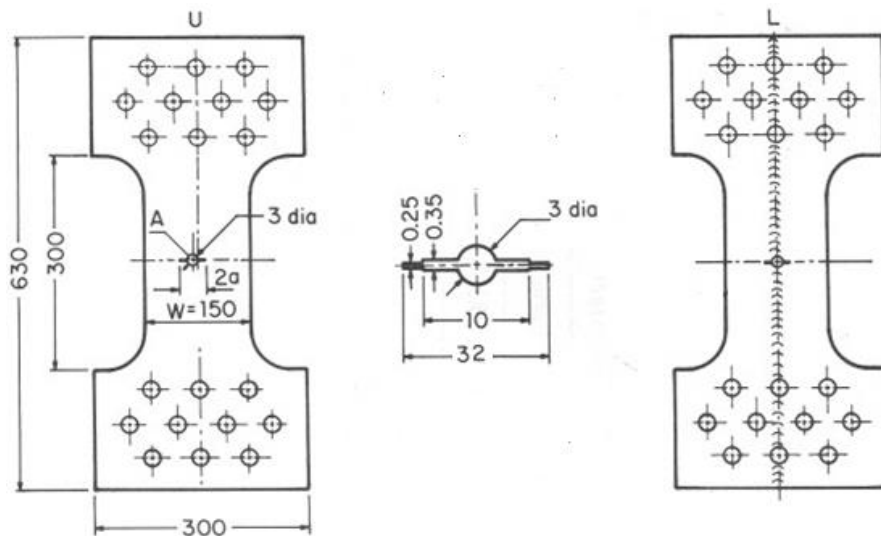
2: Modèle géométriques des éprouvettes soudées et non soudées
